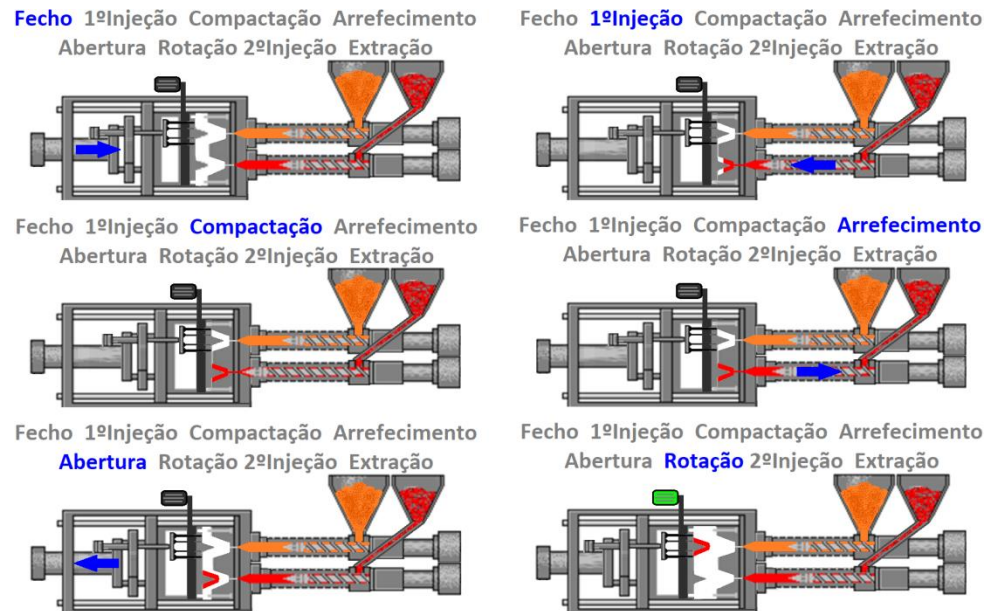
Processo de Moldação por Injeção (1) (Adaptada de [9])
